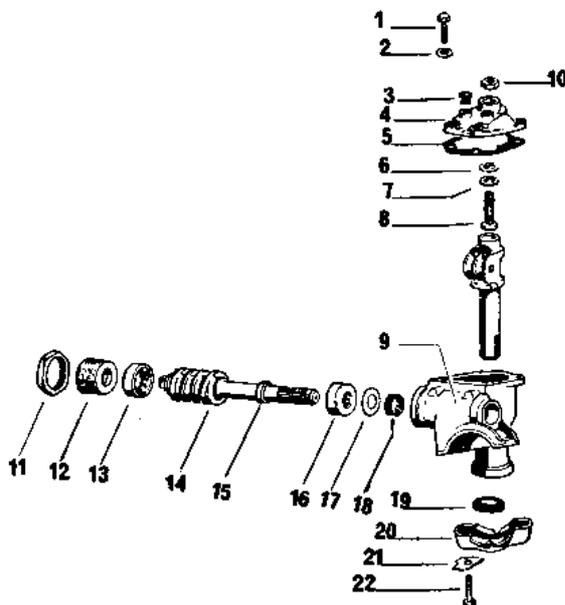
Montagebild des zerlegten Lenkgetriebes.
